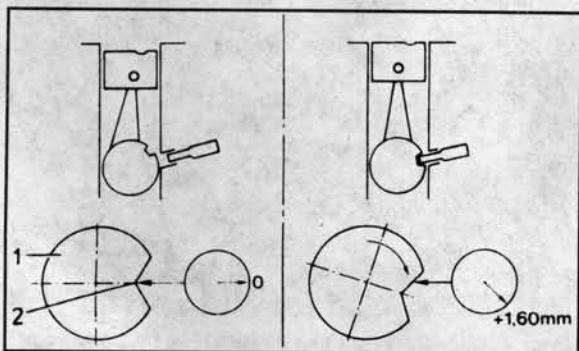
Регулировка ТНВД – установка измерительного датчика
